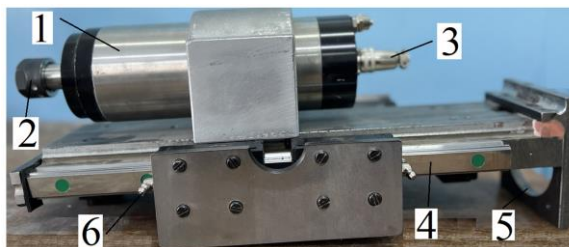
Общий вид крепления шпинделя фрезерного 3 – D станка.
